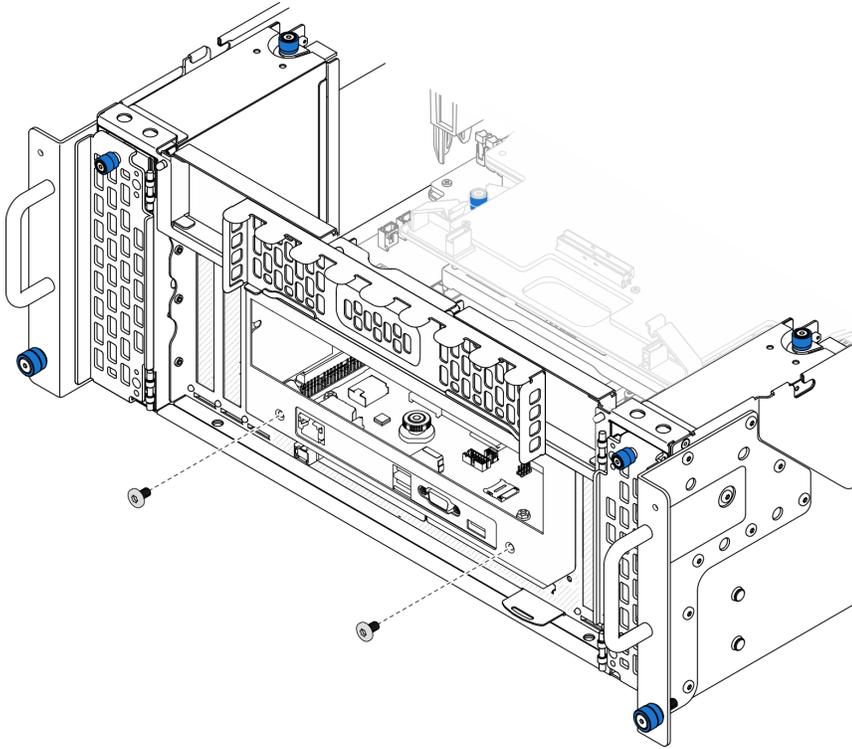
Befestigen der System-E/A-Platinen- und Interposer-Platinenbaugruppe
